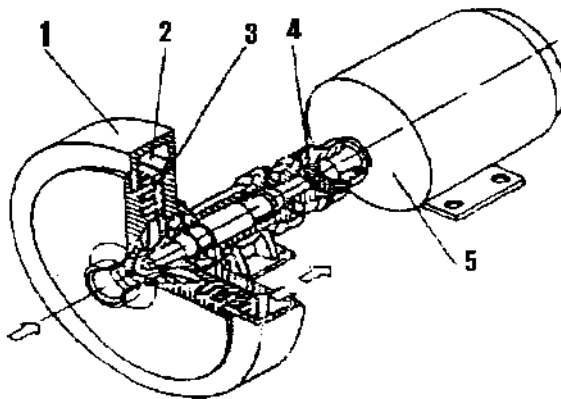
Загальний вид зубчастого гомогенізатора
